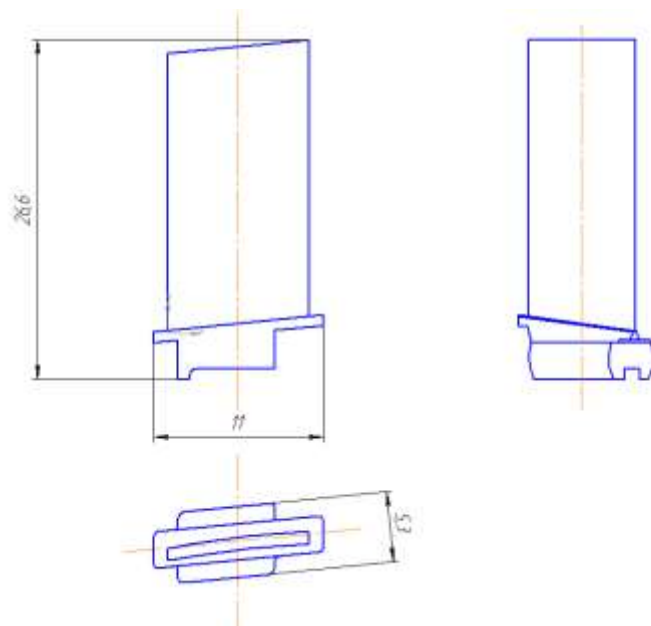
Ескіз лопатки компресора ГТД
